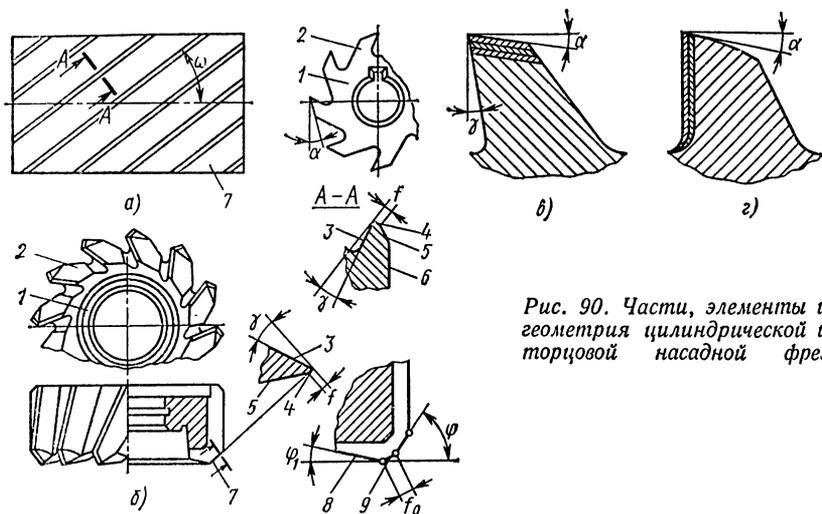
Части, элементы и геометрия цилиндрической и торцевой насадной фрез
